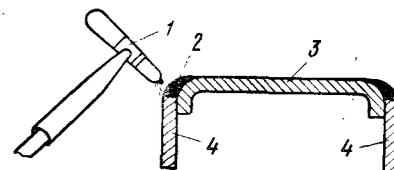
Угловое соединение крышки с корпусом конденсатора сваркой: 1 — электродержатель, 2 — сварной шов, 3 — крышка, 4 — стенка корпуса
